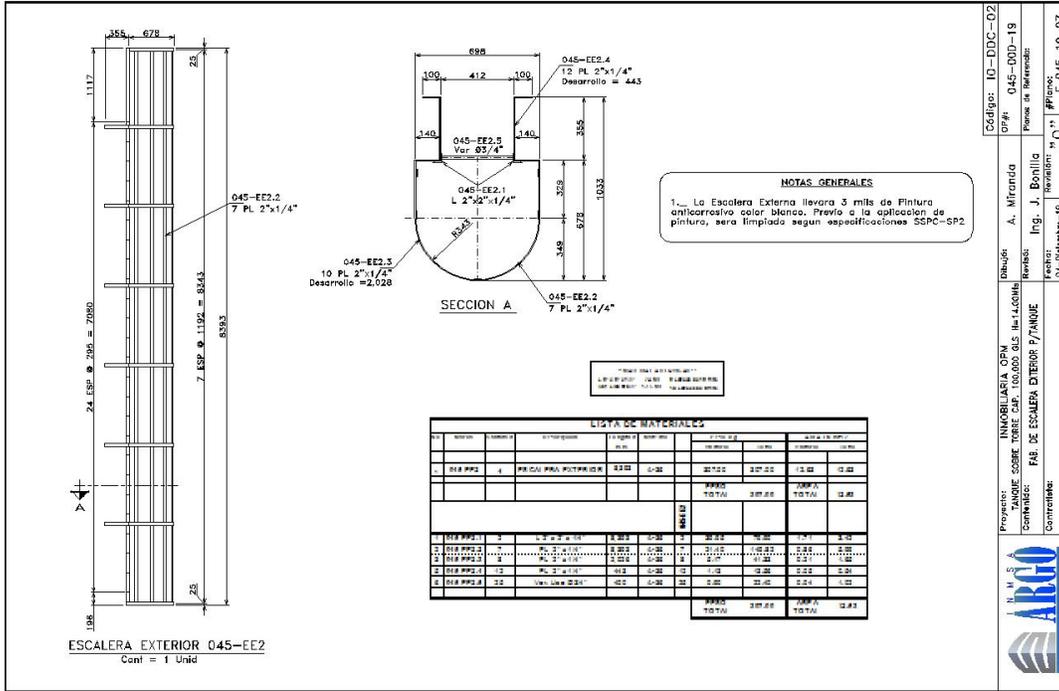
plano para la fabricación de escalera exterior para tanque elevado
